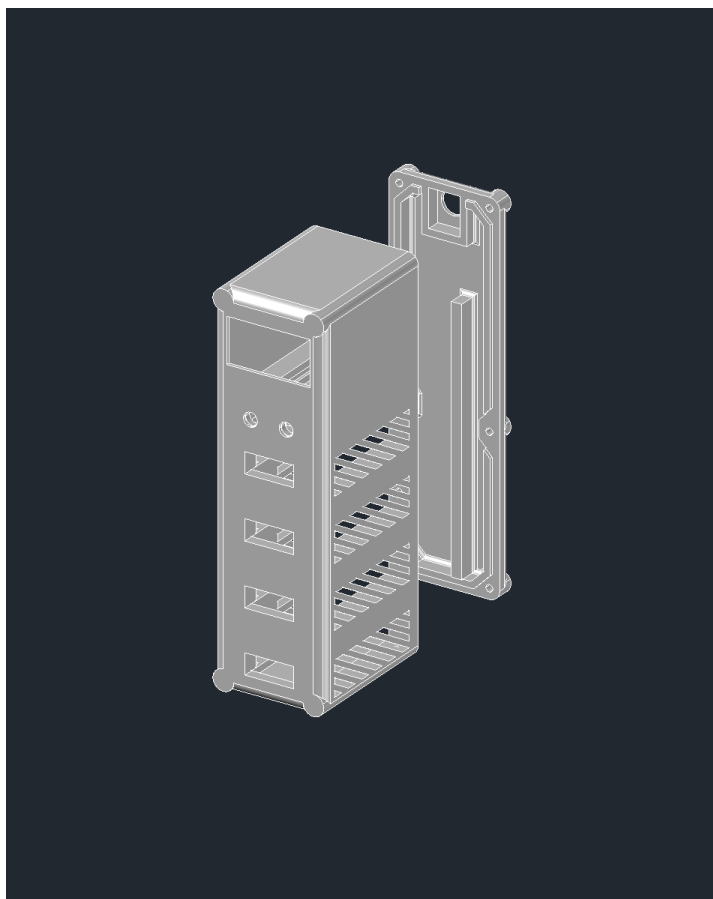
Вигляд спереду 3D моделі корпусу
